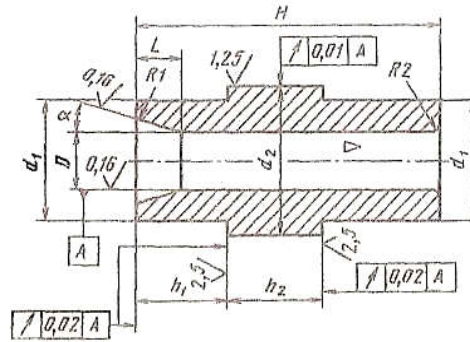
Конструкція матриці з циліндричною порожниною
